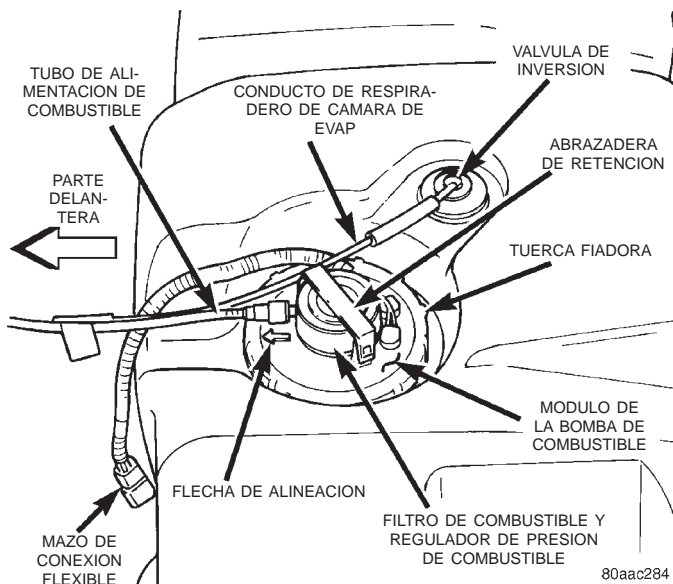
Vista superior del depósito de combustible y el módulo de la bomba de combustible
